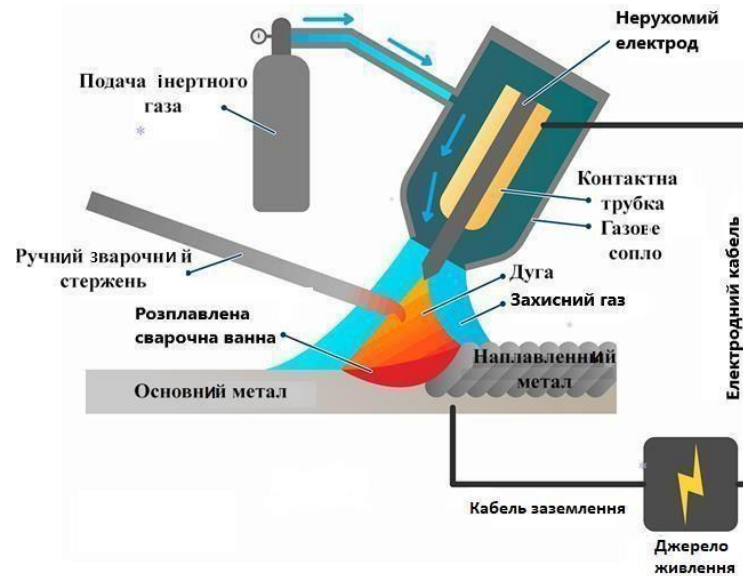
Схема ручного зварювання серед захисних газів (TIG)
